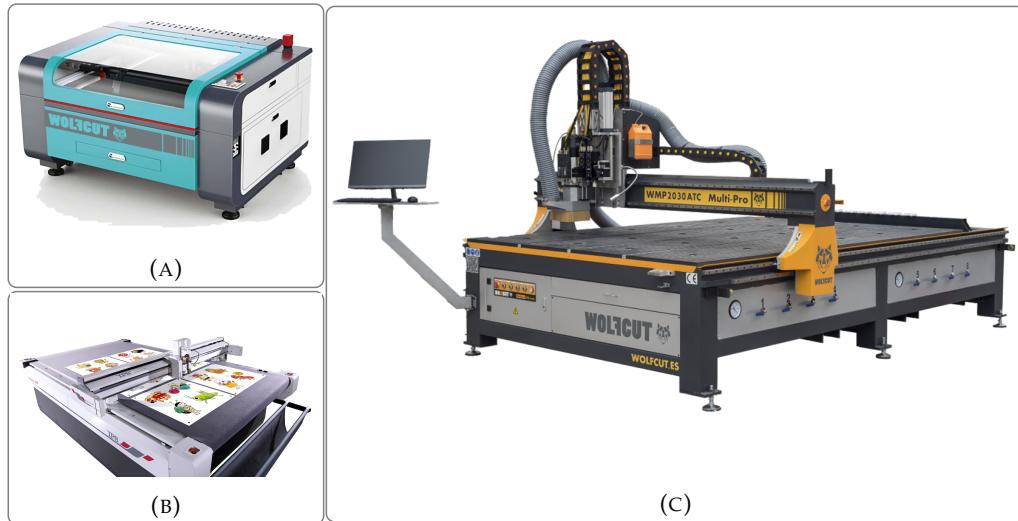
Maquinas CNC fabricadas por la empresa Wolfcut.
